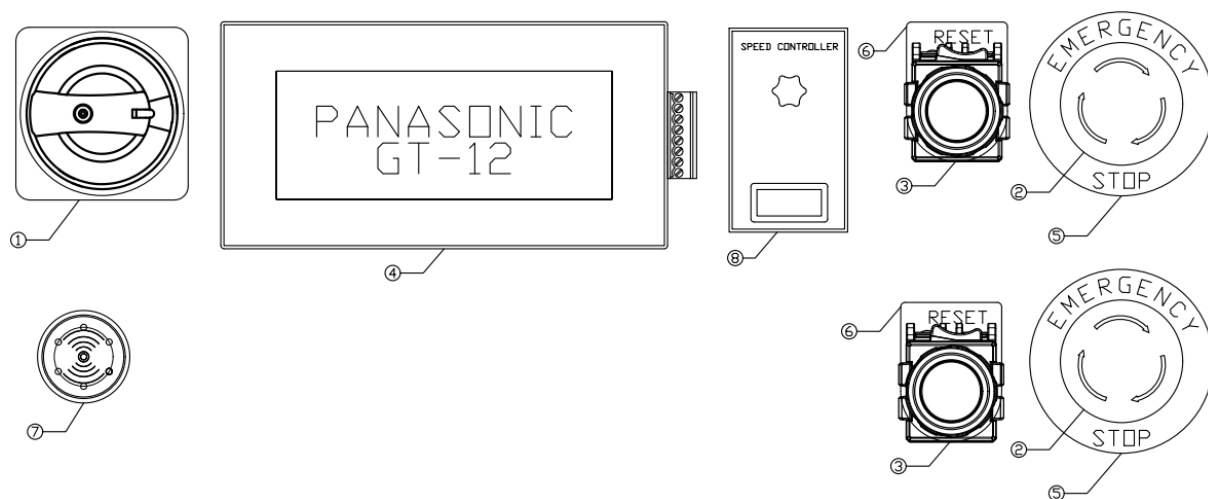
Layout bố trí thiết bị Gate Conveyor
